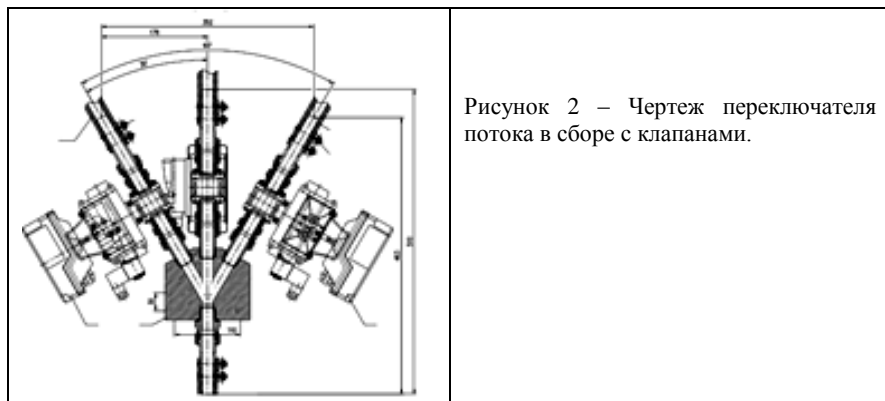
Чертеж переключателя потока в сборе с клапанами.
